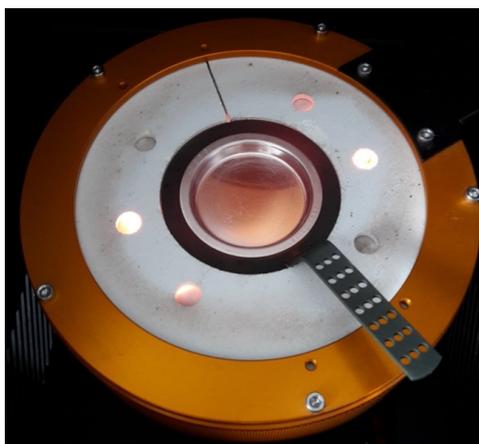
Внешний вид нагревателя изложницы с холдером и изложницей
